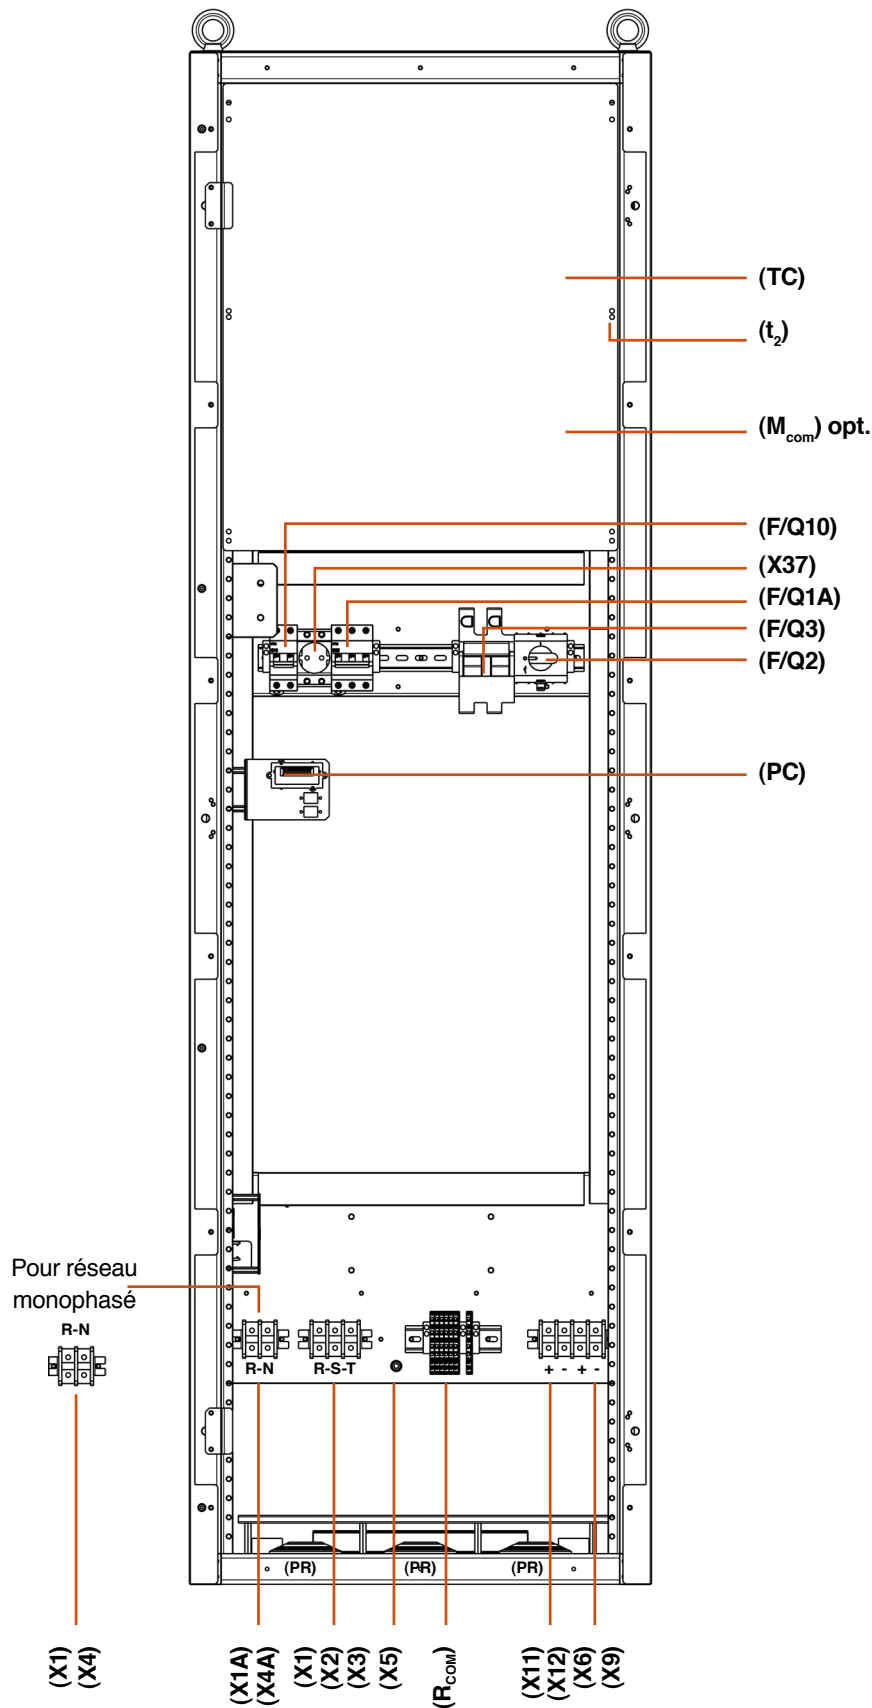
Vue de face armoire équipement de 630 x 605 x 2 115 mm sans porte (PF) et avec le couvercle de borne (TB) retiré.
